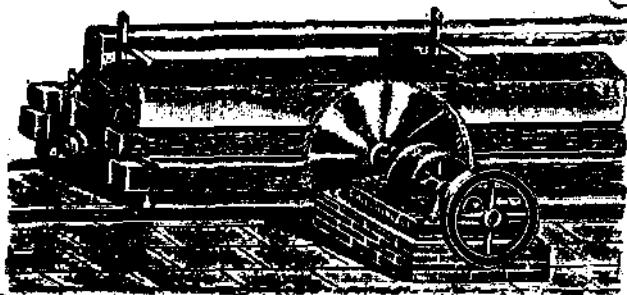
Станок с круглой пилой и платформой для ручной подачи.
